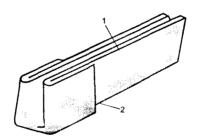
Внешний вид пазовой коробочки с манжетой для усиления: 1 — пазовая коробочка, 2 — отогнутая манжета
